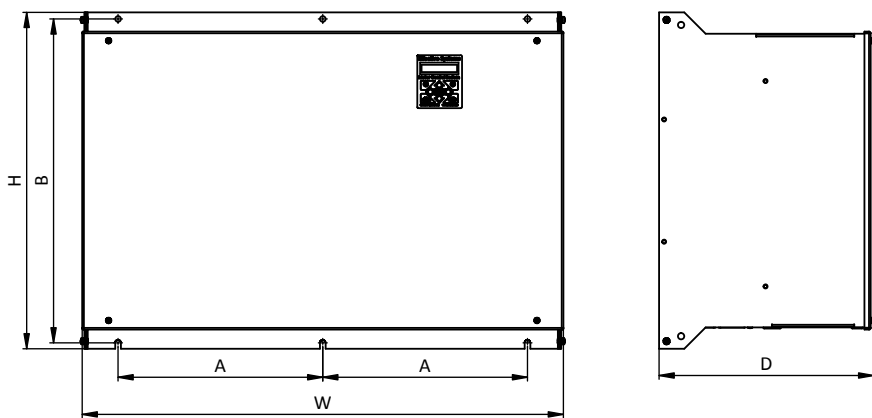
Размеры контроллера 315 - 400 кВт
